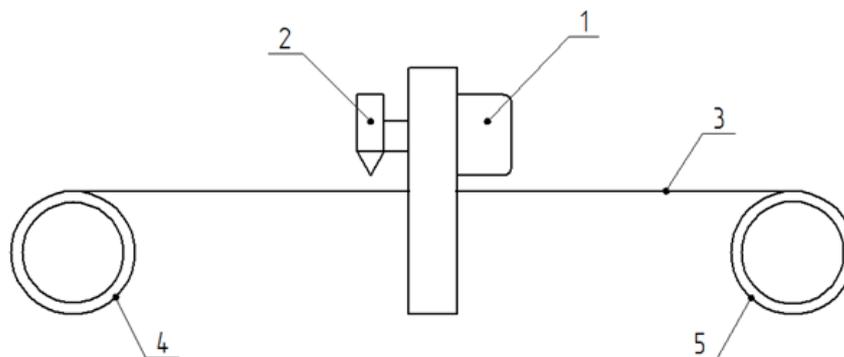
Схема устройства для оплавления поверхности проволоки:
